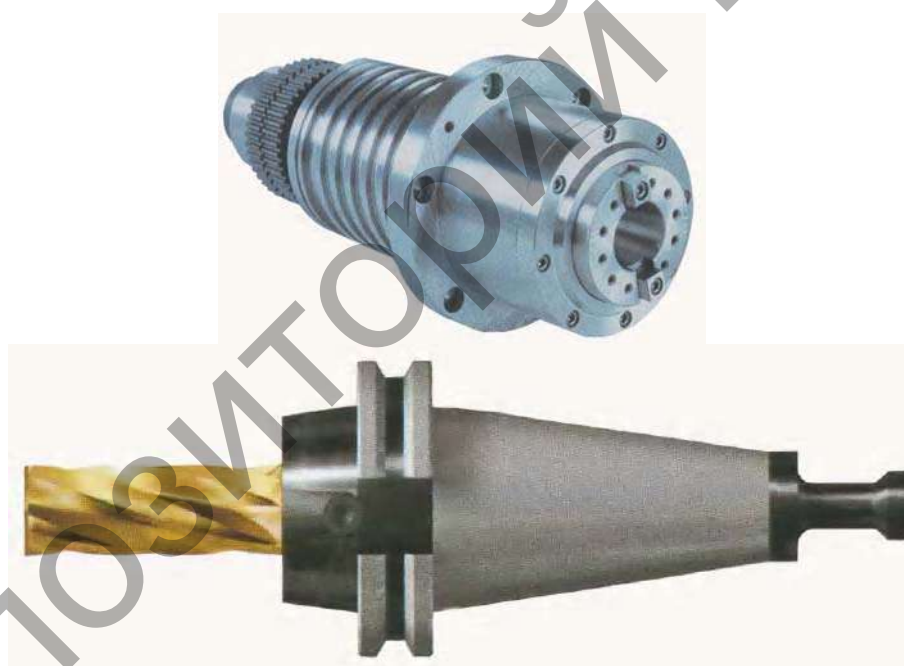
Цилиндрический и конический хвостовики оправок для крепления инструмента
